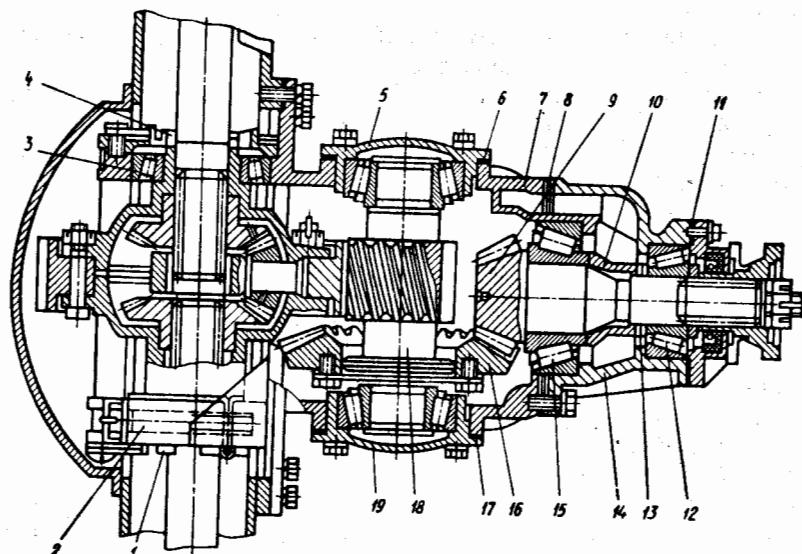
Подшипники и зацепление главной передачи автомобиля ЗИЛ-4314101
